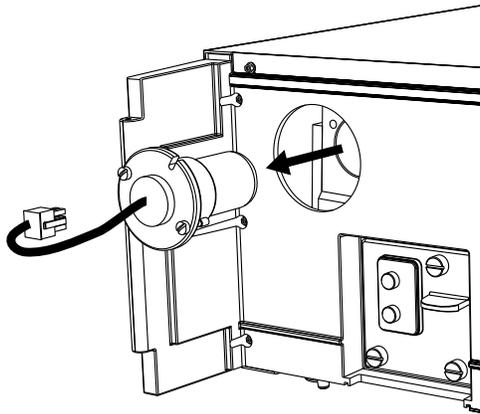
Sicherungsschrauben am Lampensockel
